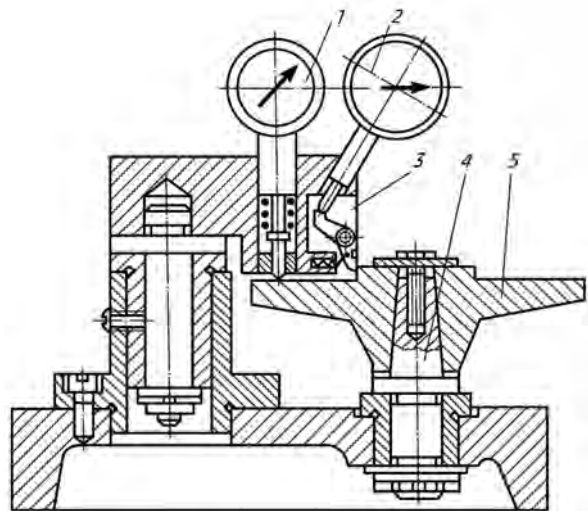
Пристосування для вимірювання торцевого та радіального биття
